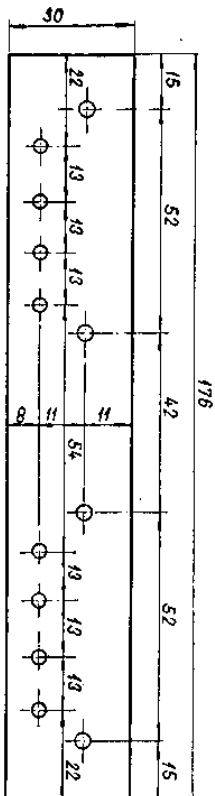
Spojovací pásek čelní a zadní stěny. Průměry otvorů jsou 3,5 mm. V místech označených čárkováním se pásek ohne do pravého úhlu
